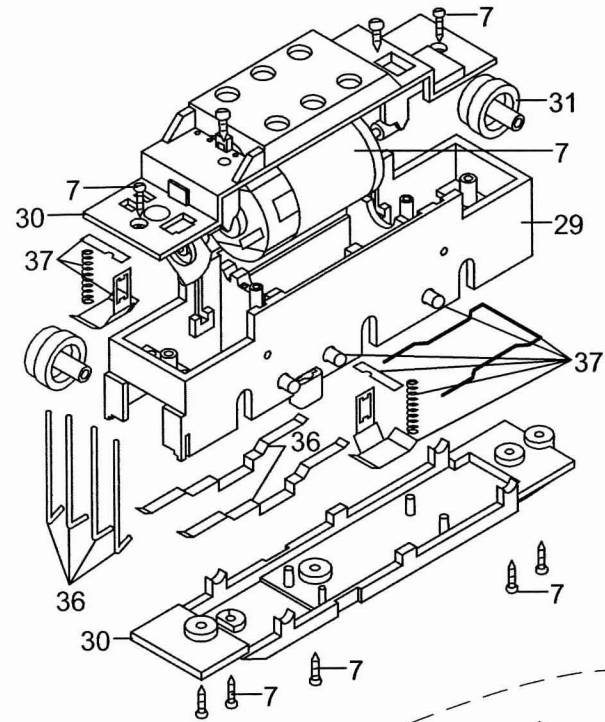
, zum Öffnen der Lok die markierten Schrauben entfernen
